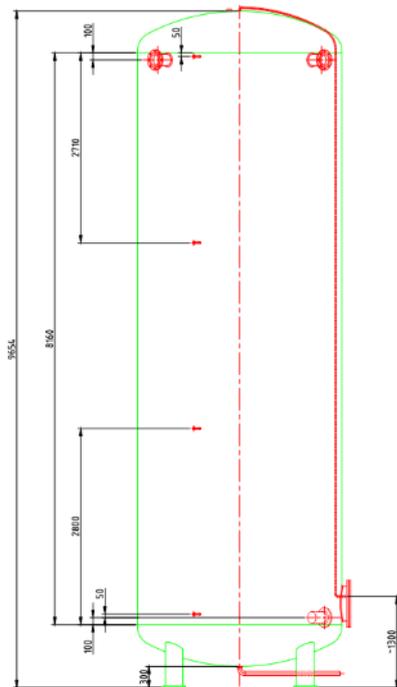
Pufferspeicher Grundriss, Variante 1
